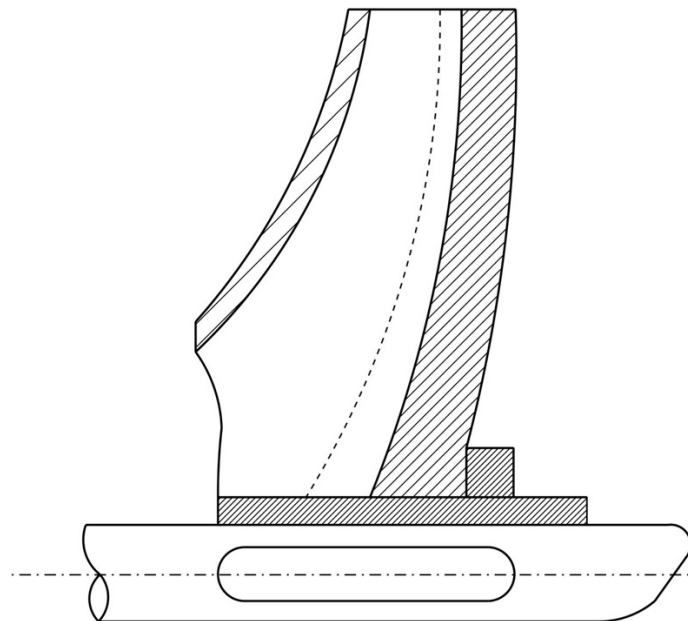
Схема підрізування робочого колеса по ширині
